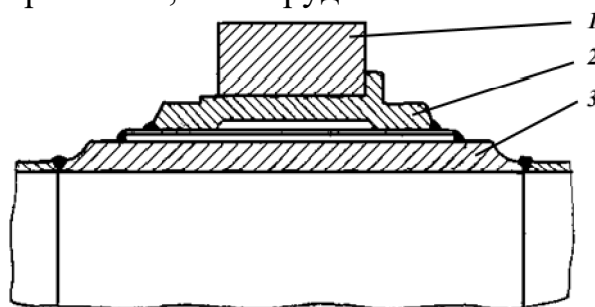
Крепление башмака к корпусу барабана электросваркой:
